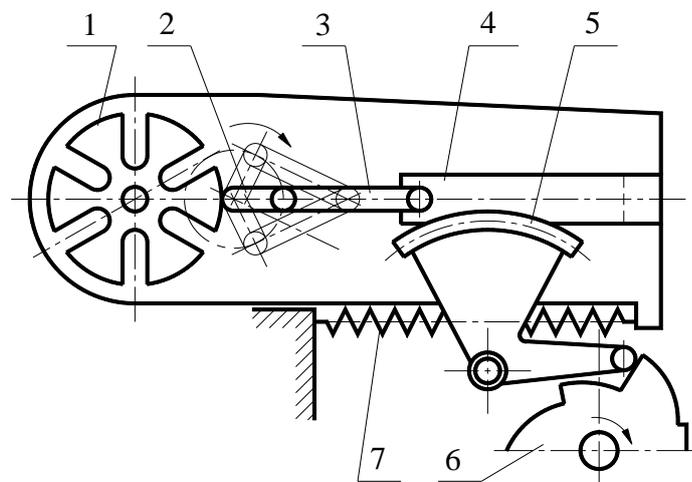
Револьверная головка одношпиндельного токарно-револьверного автомата 1Б136
